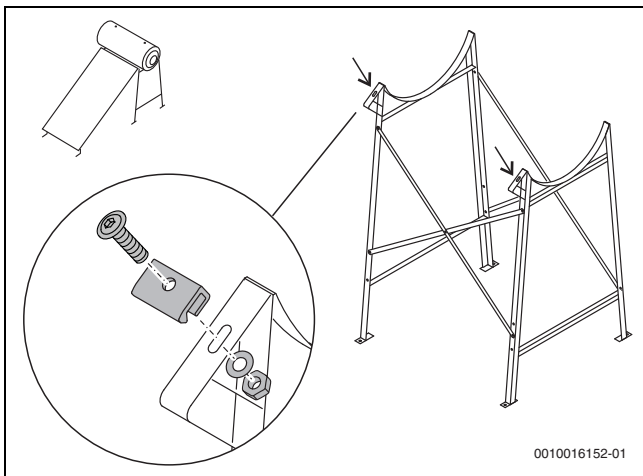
MTSS1: Atornillar el pisador directamente en el soporte de montaje
